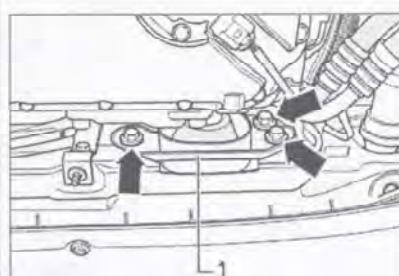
Отверните болты (стрелки) переднего упора двигателя (1) (показан для автомобиля с 6-цилиндровым двигателем).
